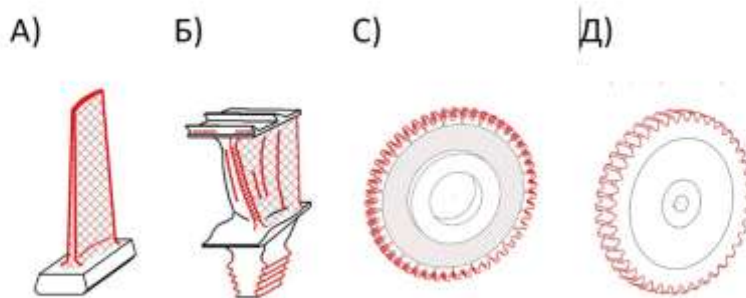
Примеры деталей газотурбинных двигателей и установок, обработка которых целесообразна с использованием фемтосекундных лазеров: лопатки компрессора (А), лопатки турбины (Б), диски (С) и зубчатые колеса (Д).
